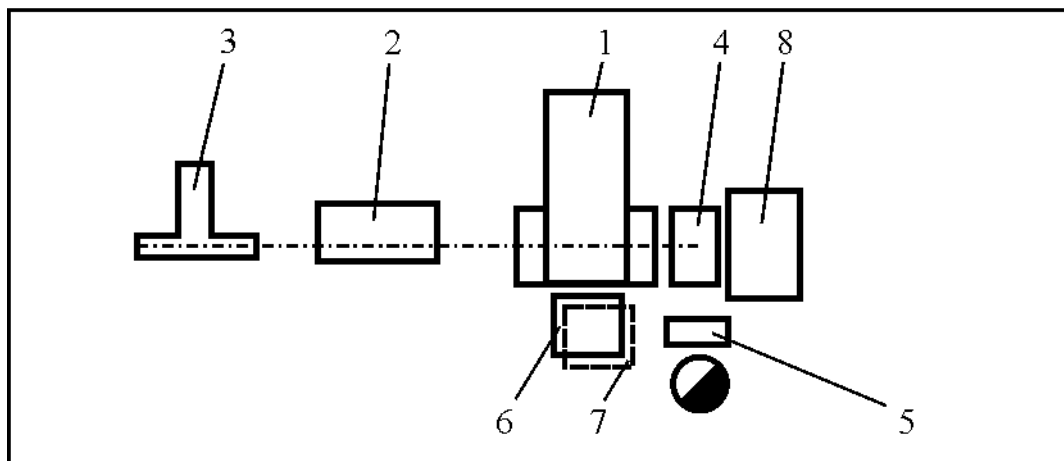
План-схема організації робочого місця оператора, що обслуговує автоматизований комплекс для штампування деталей із стрічки: 1 - кривошипний відкритий прес з автоматичною валковою подачею; 2 - правильно-розмотувальний пристрій; 3 - катушка зі стрічкою; 4 - ножиці для здріблювання відходів від стрічки; 5 - пульт керування; 6 - бункер для деталей; 7 - бункер для відходів (встановлено у приямку преса); 8 - бункер для відходів від стрічки
